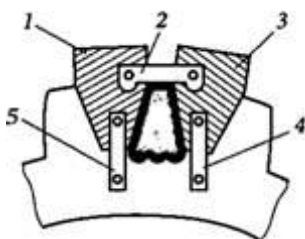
Схема наплавки изношенного зуба: 1,3 – медные пластины; 2,4,5 – крепежные планки
